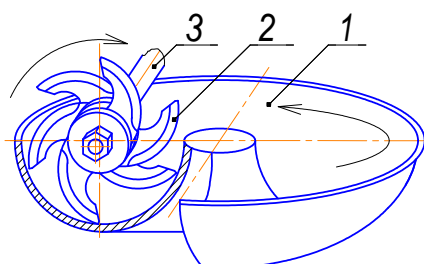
Принципова схема кутера: 1 – чаша; 2 – ножова головка; 3 – ножовий вал
